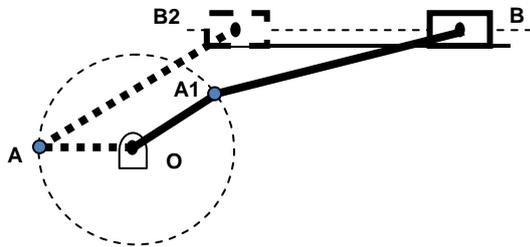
Cadena cinemática de tipo cerrada, para el movimiento horizontal del carro porta cilindros
